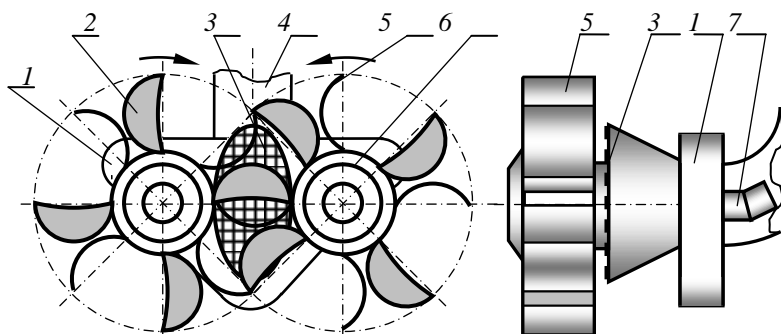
Схема двухроторного черпакового разрыхлителя.
